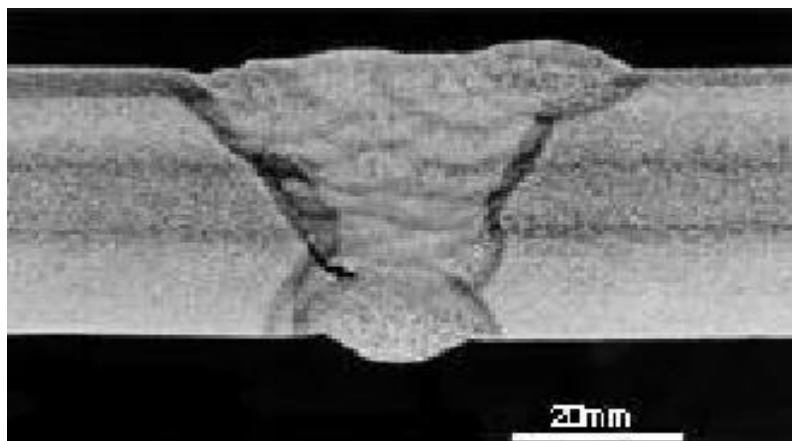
Manque de fusion dans le flanc de la soudure.
